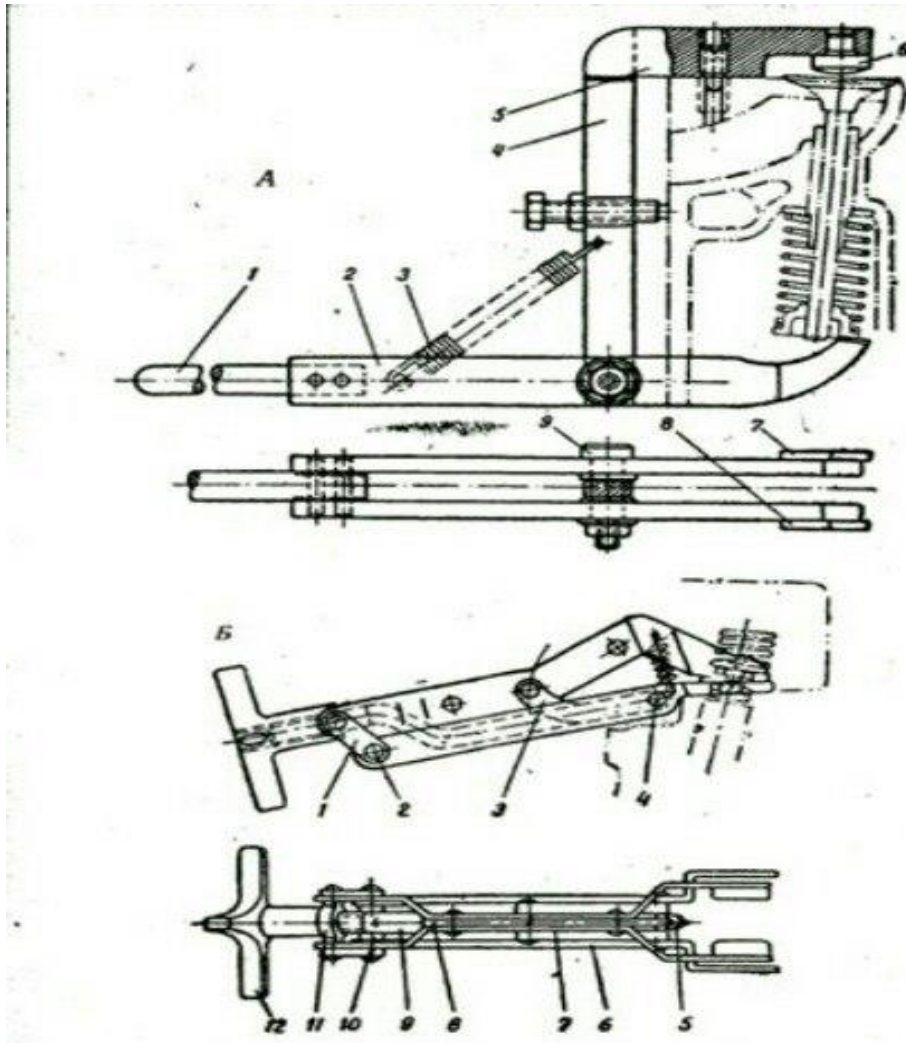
Пристосування для зняття і установки пружин клапанів:
